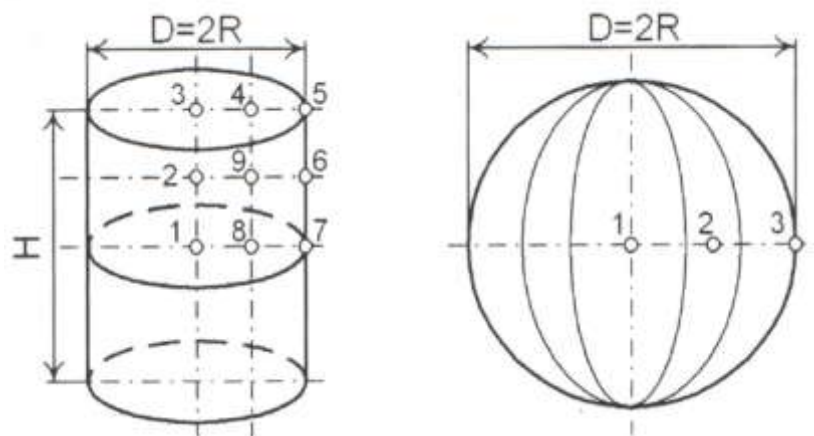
Характерные точки при нагреве цилиндрической и шаровой заготовки
